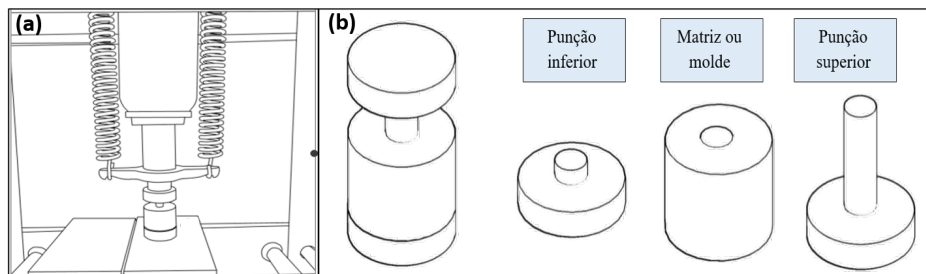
Etapa de compactação: (a) prensa hidráulica uniaxial; (b) molde de aço.
